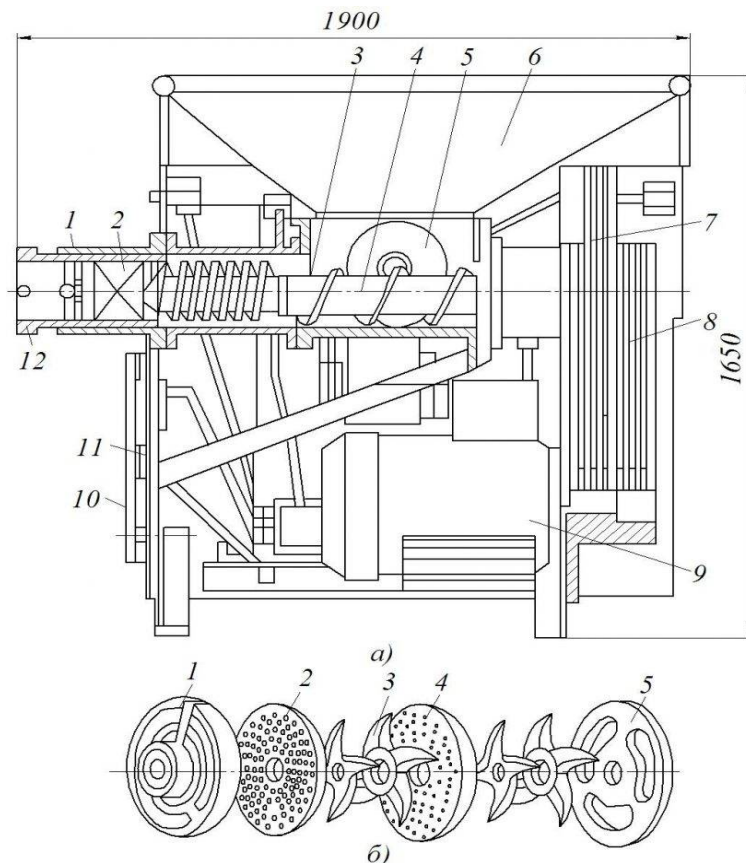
Схема вовчка: а – загальний вид з осьовим розрізом (1 – підпирні ґрати; 2 – ріжучий механізм; 3 – ножовий вал; 4 – шнек; 5 – одновиткова лопать; 7, 8 – клинопасова передача; 9 – електродвигун; 10 – майданчик для санітарної обробки; 11 – жолоб; 12 – трубчаста насадку); б – ріжучий механізм вовчка (1 - підпирна решітка; 2 – вихідна ножова решітка; 3 – ножі; 4 – проміжна решітка; 5 – приймальна решітка)
